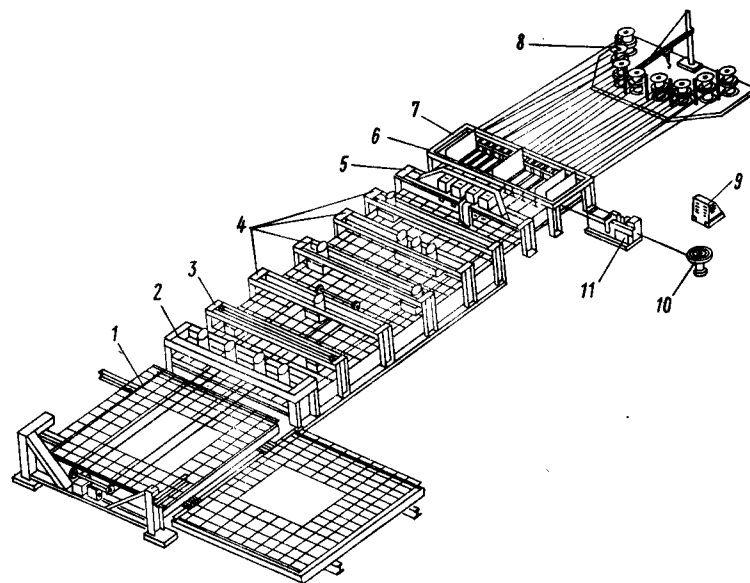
Автоматизированная линия для сварки широких сеток:
